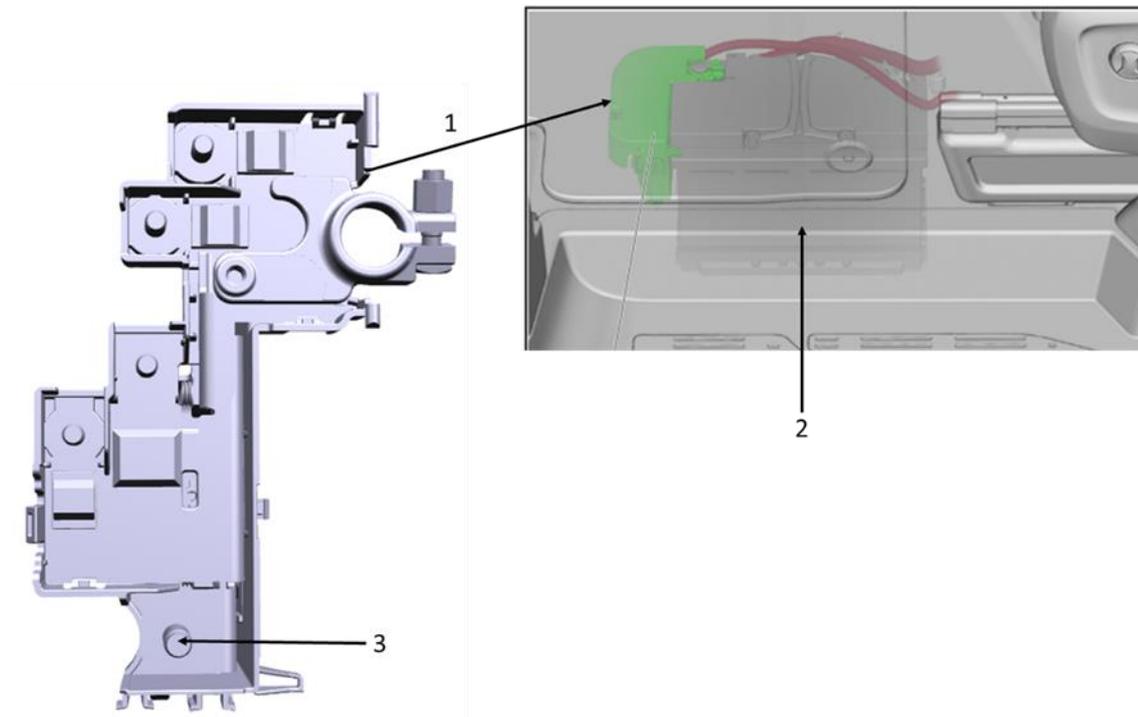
platine porte-fusibles A sur la protection centrale de batterie située dans le plancher du véhicule devant le siège gauche.
